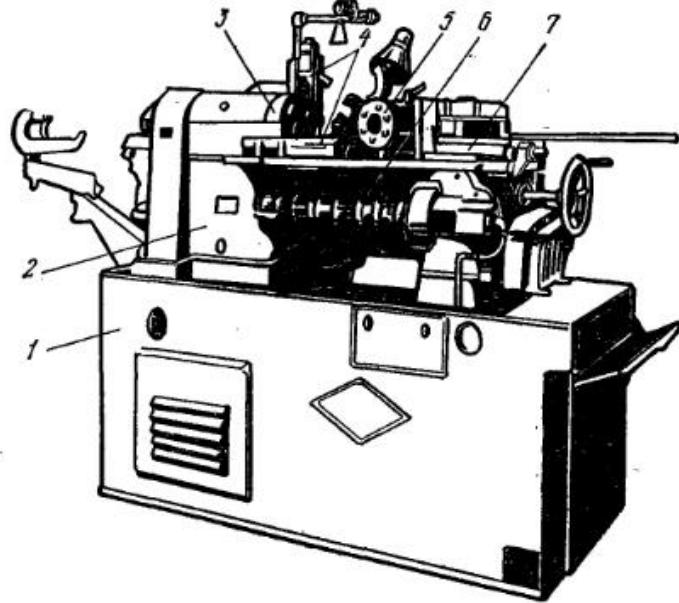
Общий вид и основные узлы токарно-револьверного автомата:
